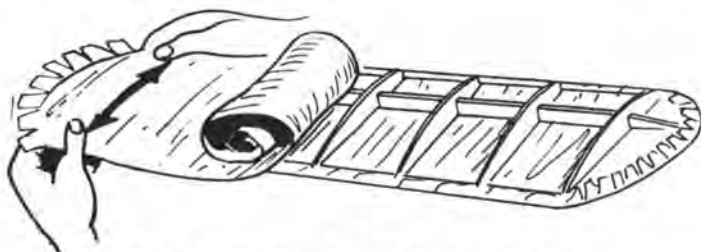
Entoilage de l'extrados d'un plan-fixe.
